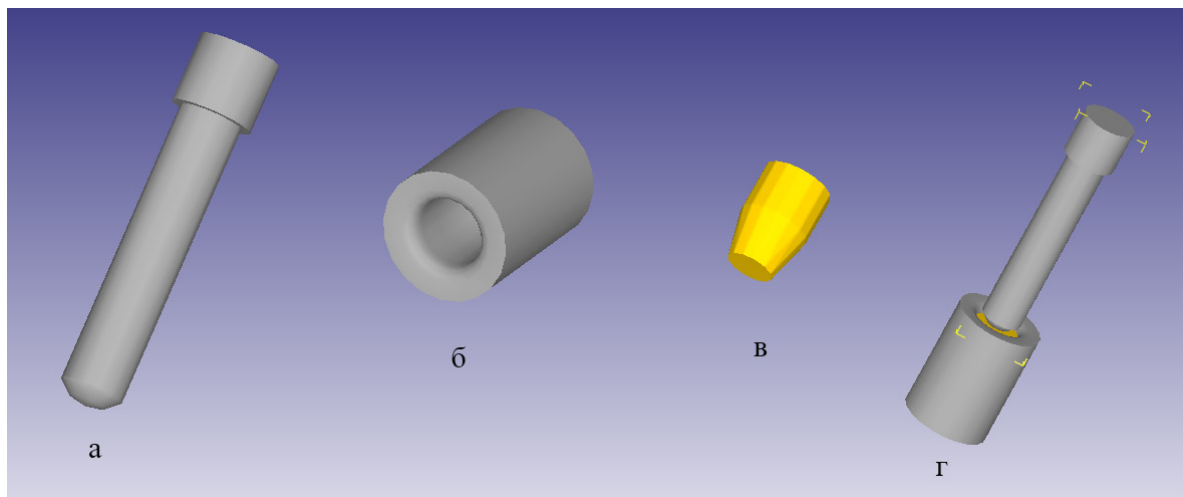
Штамповая оснастка с заготовкой: а - пуансон, б – матрица, в – заготовка (обрабатываемая деталь), г – оснастка и заготовка в сборе.
